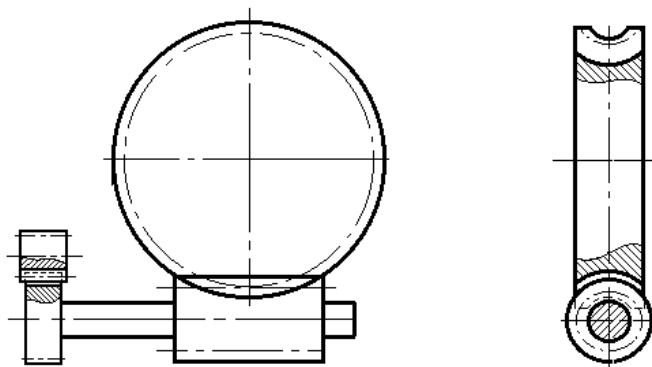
Схема расположения ступеней двухступенчатого цилиндро-червячного редуктора
